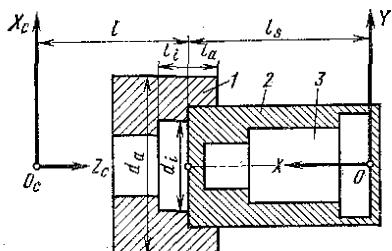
Параметры установка, указываемые в EXAPT 2 для связи систем координат детали и станка
